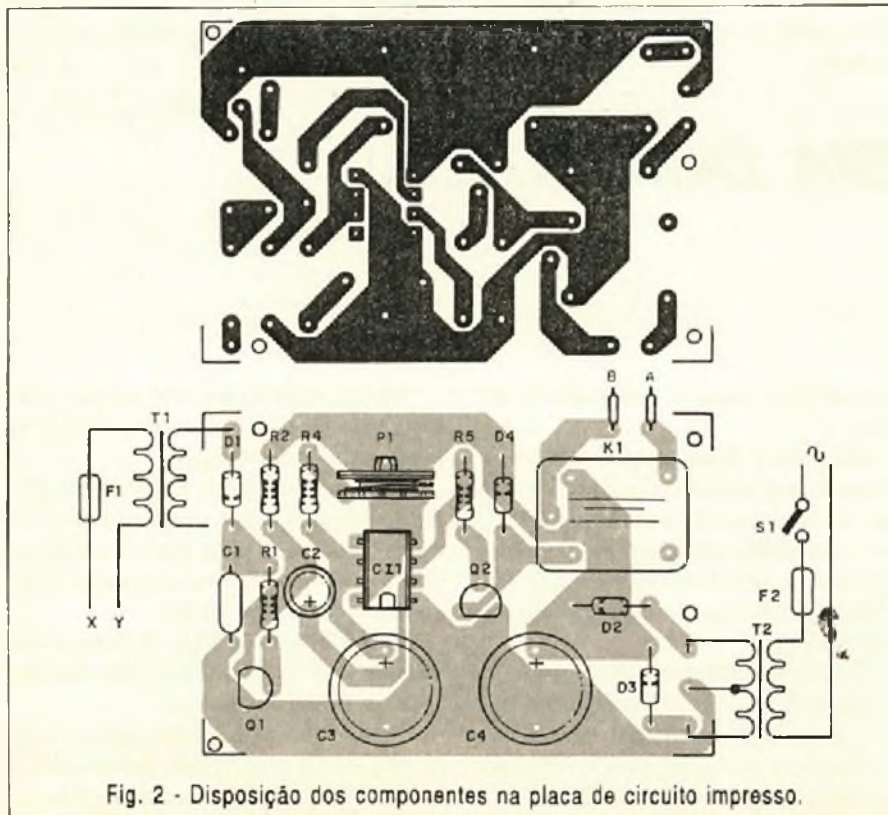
Disposição dos componentes na placa de circuito impresso.
